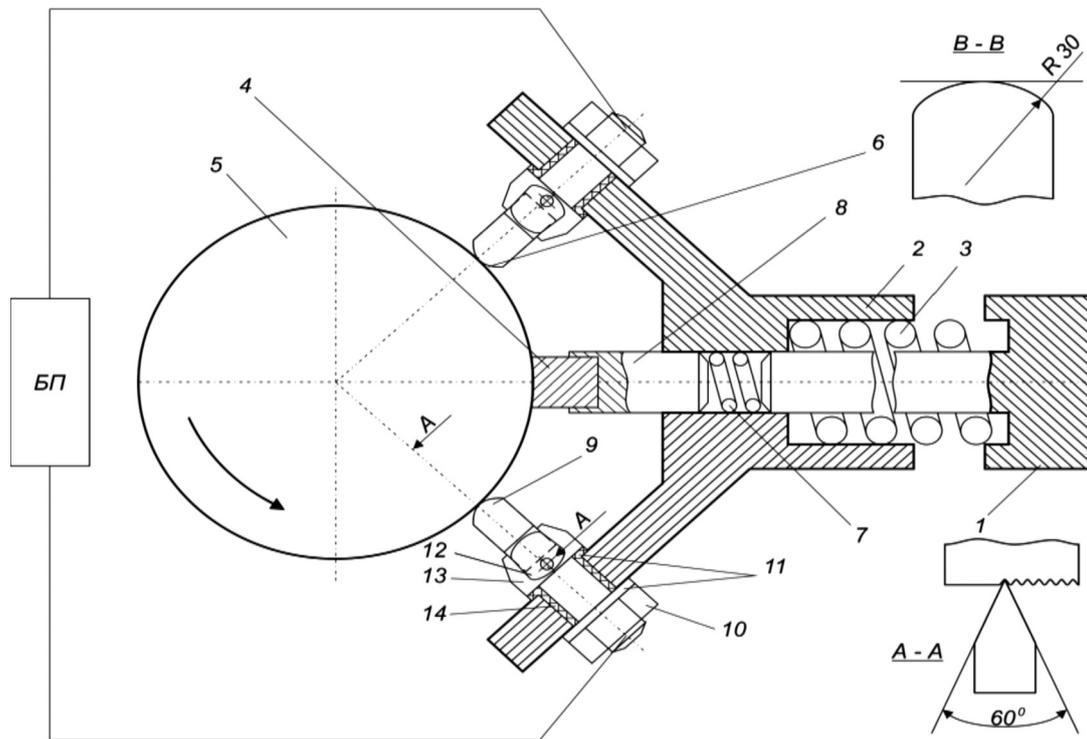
Инструмент для АФЭМО натиранием твердосмазочного материала
